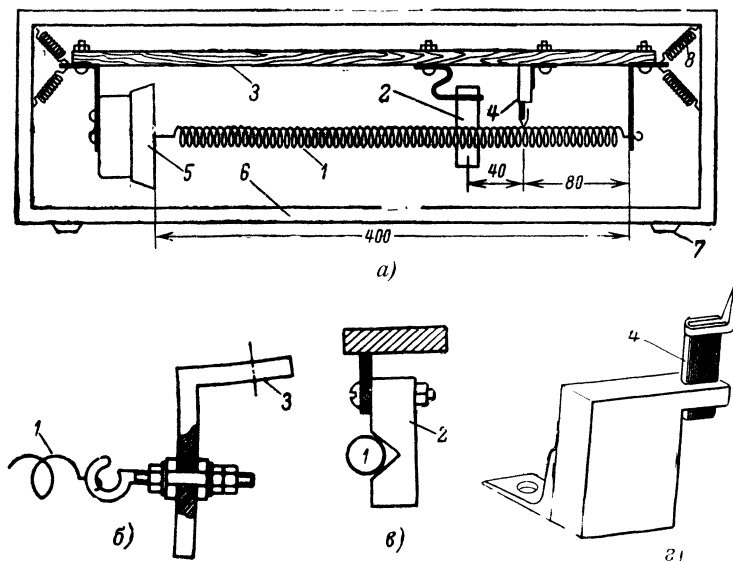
Любительская конструкция однопружинного ревербератора. а—общий вид; б—крепление пружины к опоре ревербератора; в—размещение пружины в демпфере; г—стойка крепления звукоснимателя с хомутиком.
